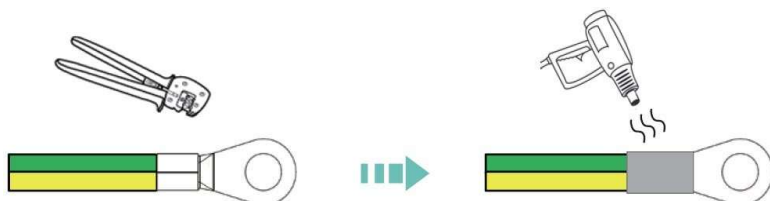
Engarzado y sellado del cable de puesta a tierra
